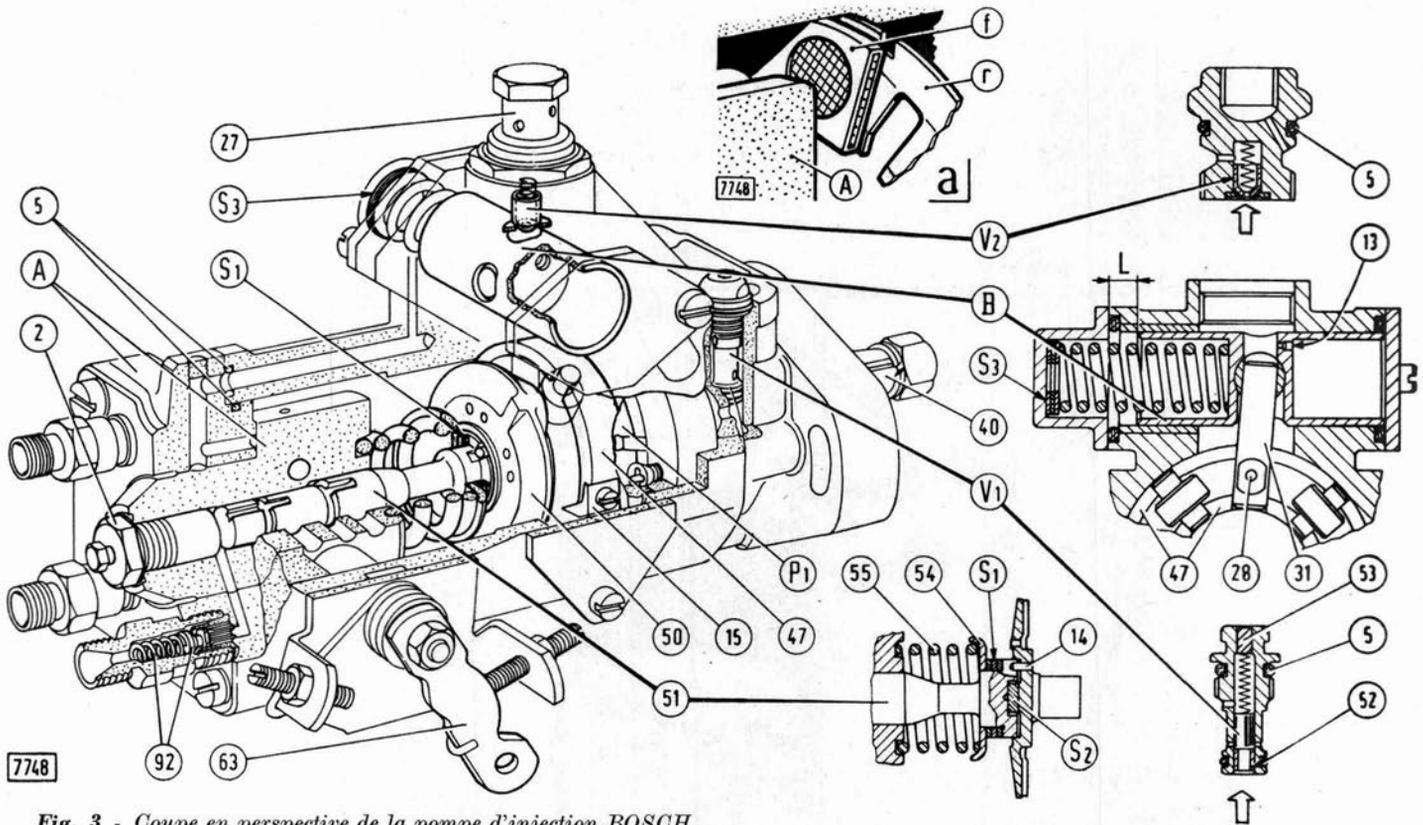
Coupe en perspective de la pompe d'injection BOSCH.
